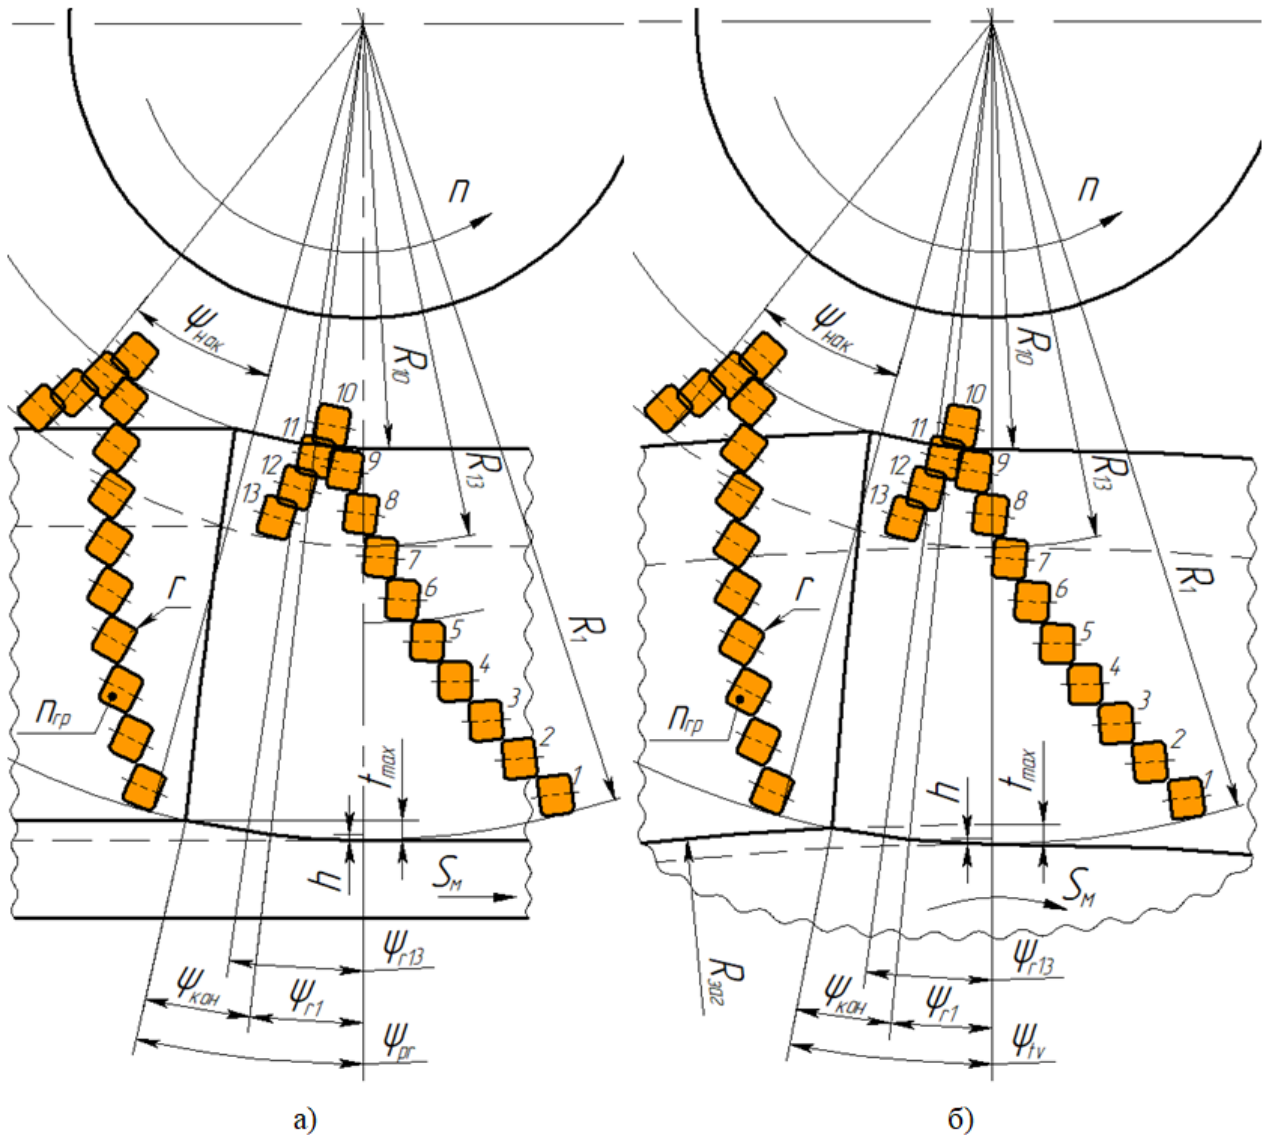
Схема попутного фрезерования: профиля головки рельсов (а) и колесных пар (б), где S_M – подача заготовки; n – частота вращения фрезы; $n_{гр}$ – количество режущих пластин на одном ноже; R_1 – максимальный радиус фрезы; R_{10} – минимальный радиус фрезы; R_{13} – последний радиус фрезы; t_{max} – максимальная глубина резания; r – радиус округления режущих кромок пластин; h – глубина смятия материала заготовки ($h = r$).
